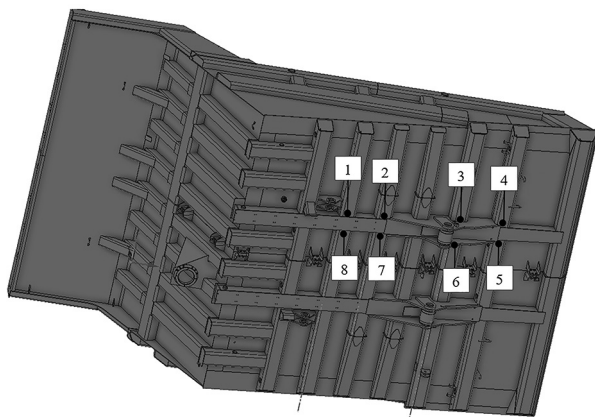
Зоны установки тензорезисторов на несущих конструкциях кузова карьерного самосвала
